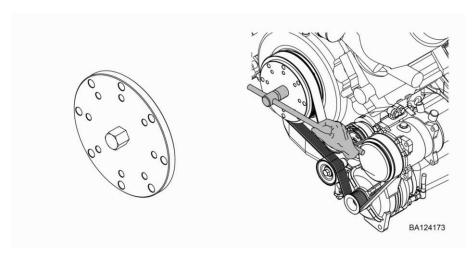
Dispositivo de giro: montaje de la caja del volante de impulsión, herramienta especial Nr. 31
